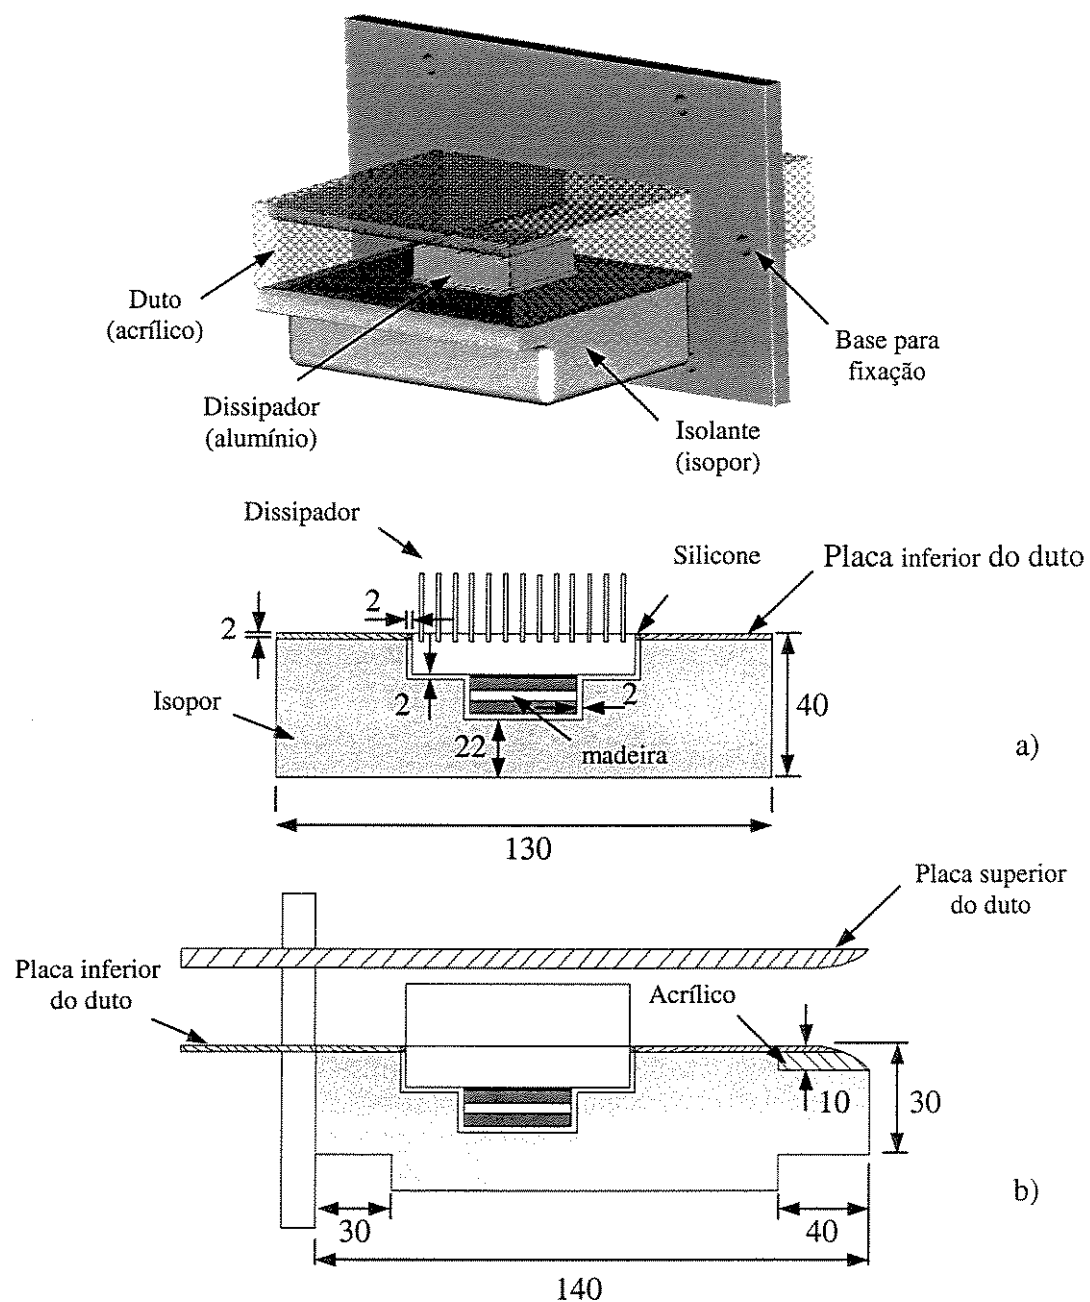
Montagem do conjunto térmico no duto (dimensões em mm): a) Vista frontal; b)
